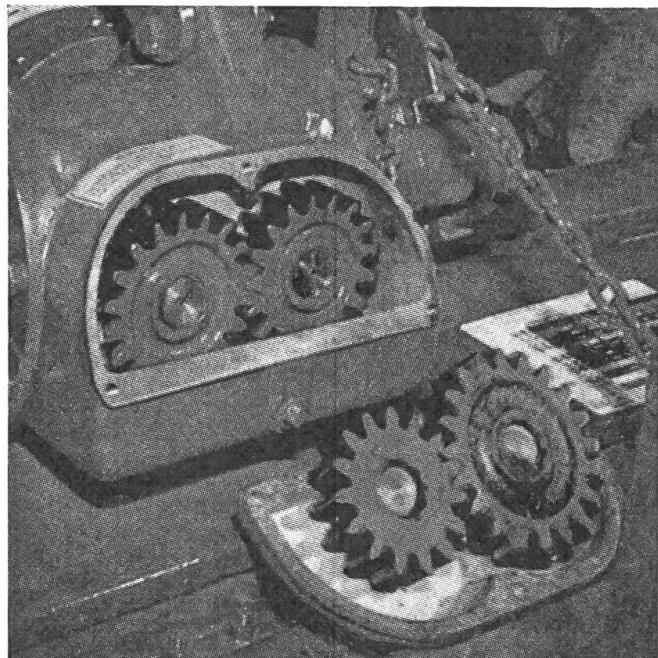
Wechselgetriebe einer Bodenfräse: Durch Auswechseln der Zahnradpaare kann die Fräswellen-Drehzahl eingestellt werden.
